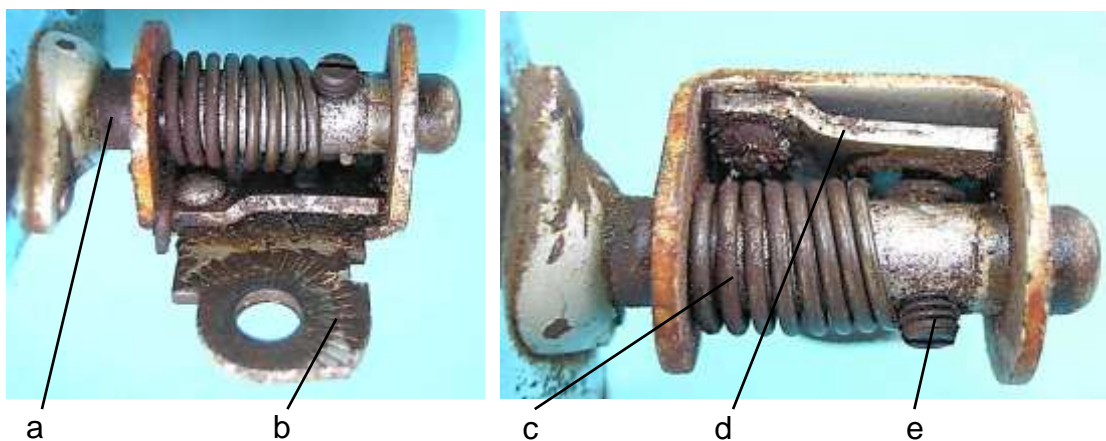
Kippvorrichtung: a) Drehbolzen mit Flansch, b) Basisblech, c) Druckfeder, d) Kulissenblech, e) Sperrstift (Madenschraube)
